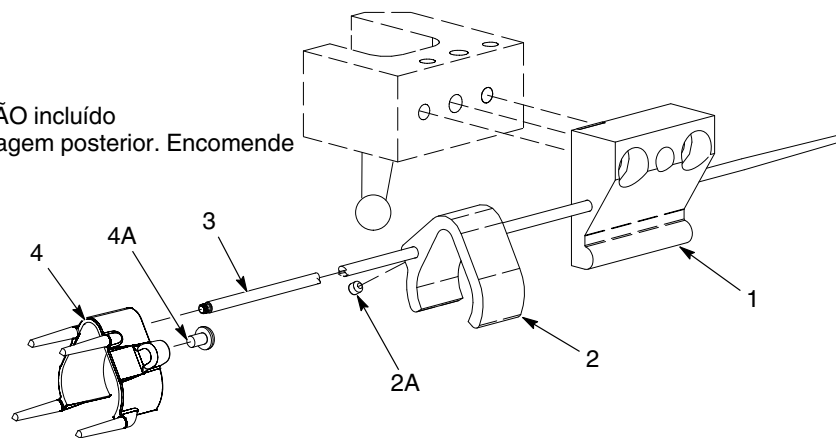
Kit de colector de iões opcional para montagem posterior em pistola com tubo de suporte
